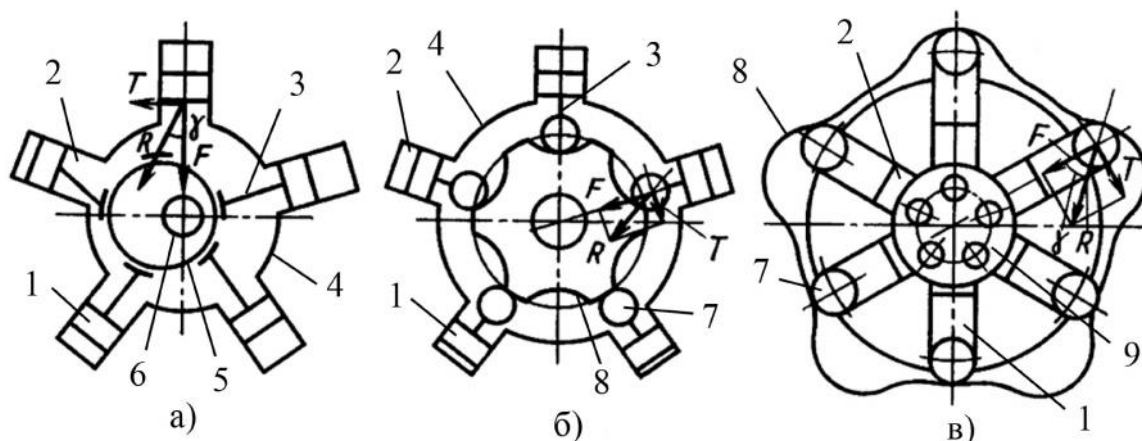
Схемы высокомоментных гидромоторов: а - РПГ однократный; б - РПГ многократный с внутренним копиром; в - РПГ многократный с внешним копиром; 1 – поршень; 2 – цилиндр; 3 – шатун с опорным башмаком; 4 – корпус; 5 – эксцентрик; 6 – выходной вал; 7 – опорные ролики; 8 – копир; 9 – распределительный вал
